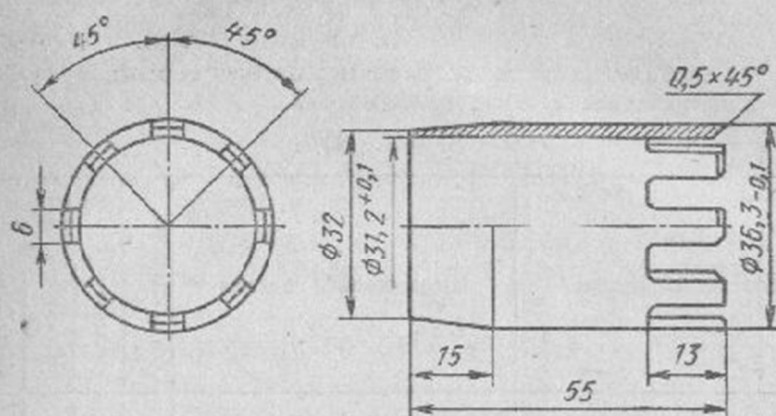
Чертеж втулки — приспособления для установки вторичного вала в сальник
